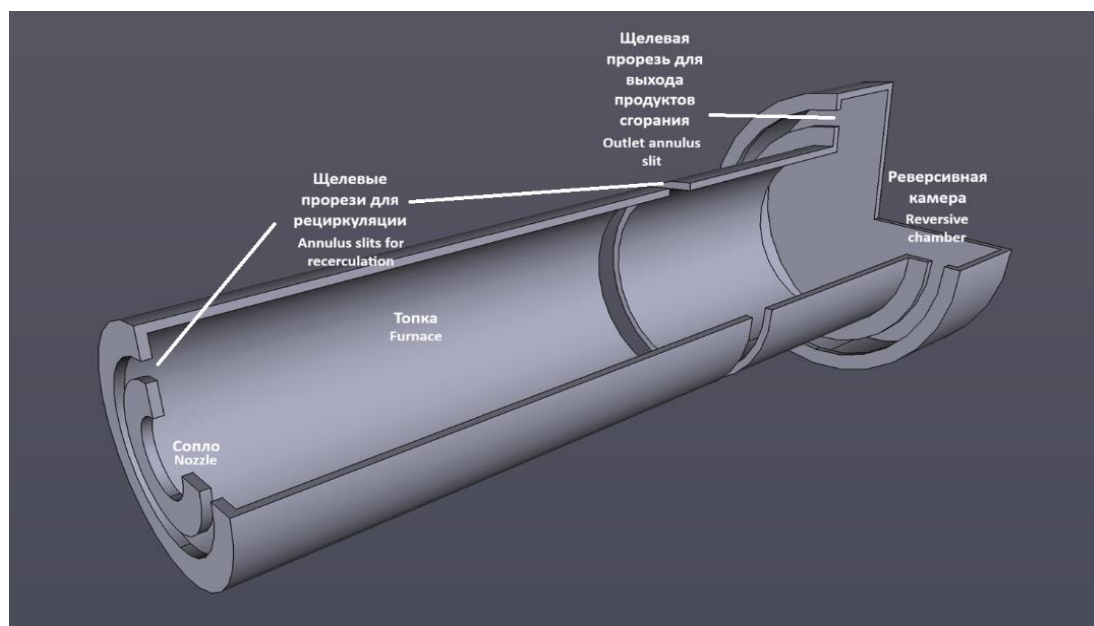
Топка котлоагрегата вместе с реверсивной камерой.
